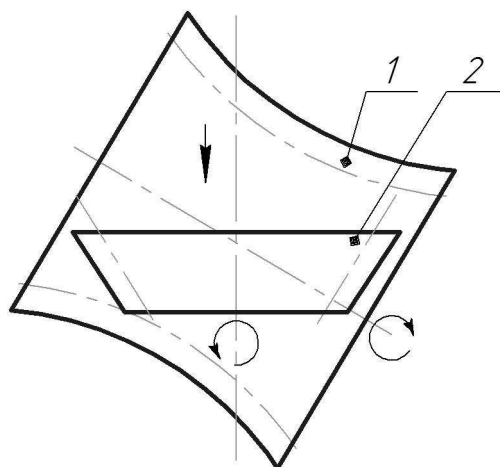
Схема изготовления квазигиперболических зубчатых колес
